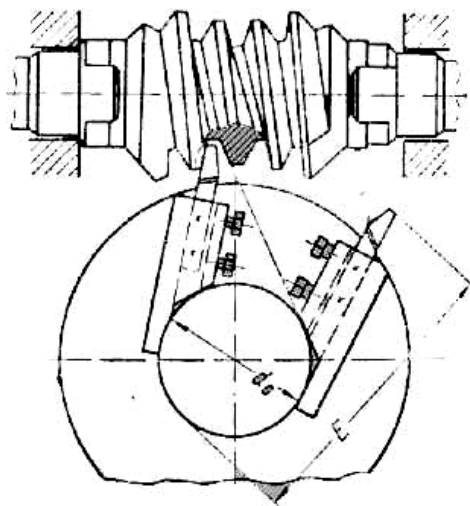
Установка резцов при нарезке глобоидного червяка одним резцом [4]
